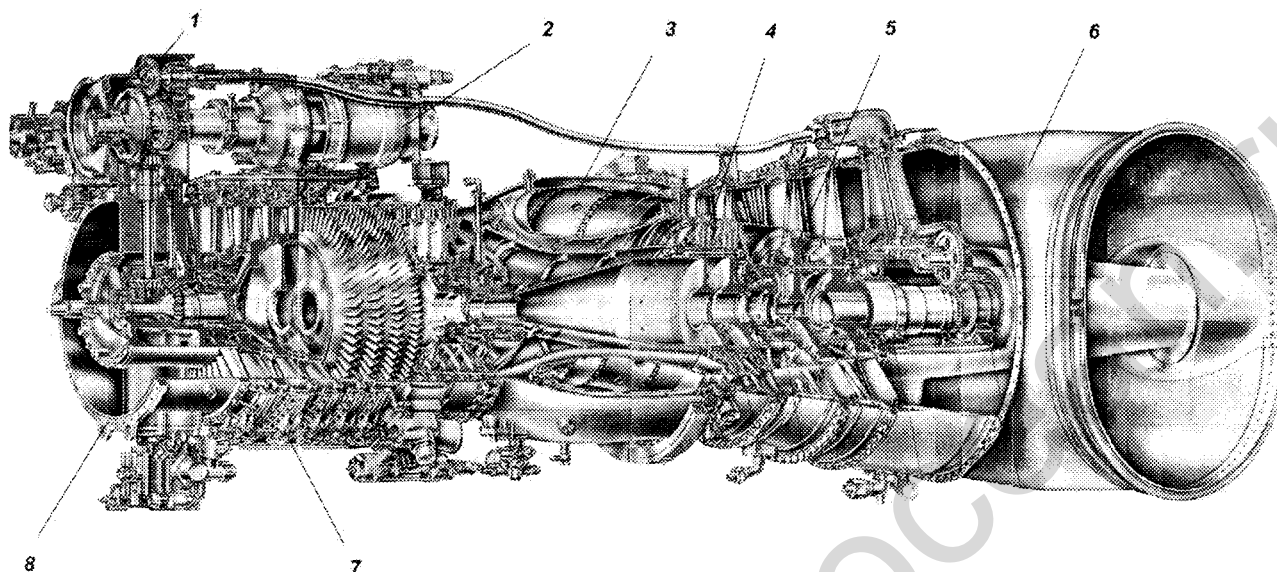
Компоновочная схема двигателя ТВЗ-117В:
